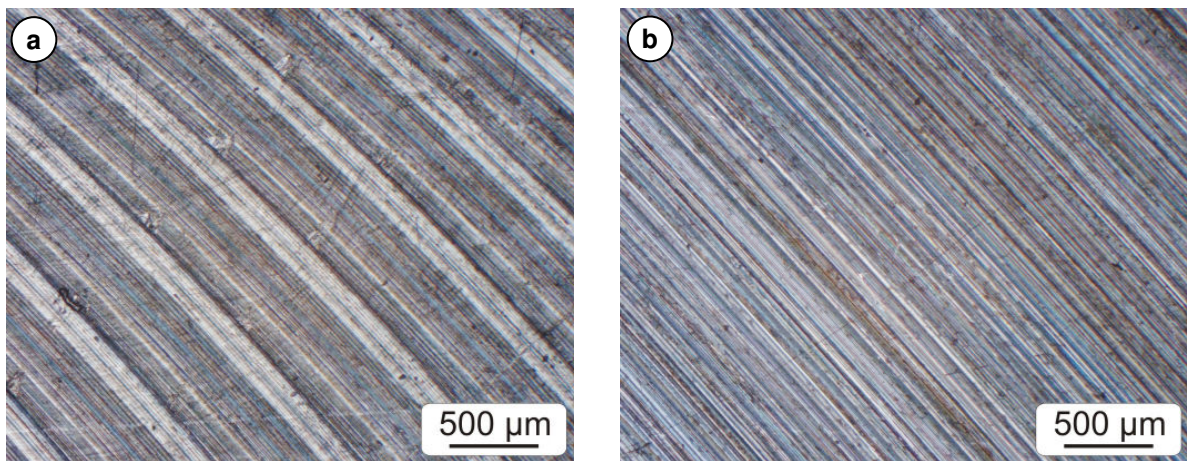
Aufsicht auf die gefräste Oberfläche des unteralterten Gefüges
